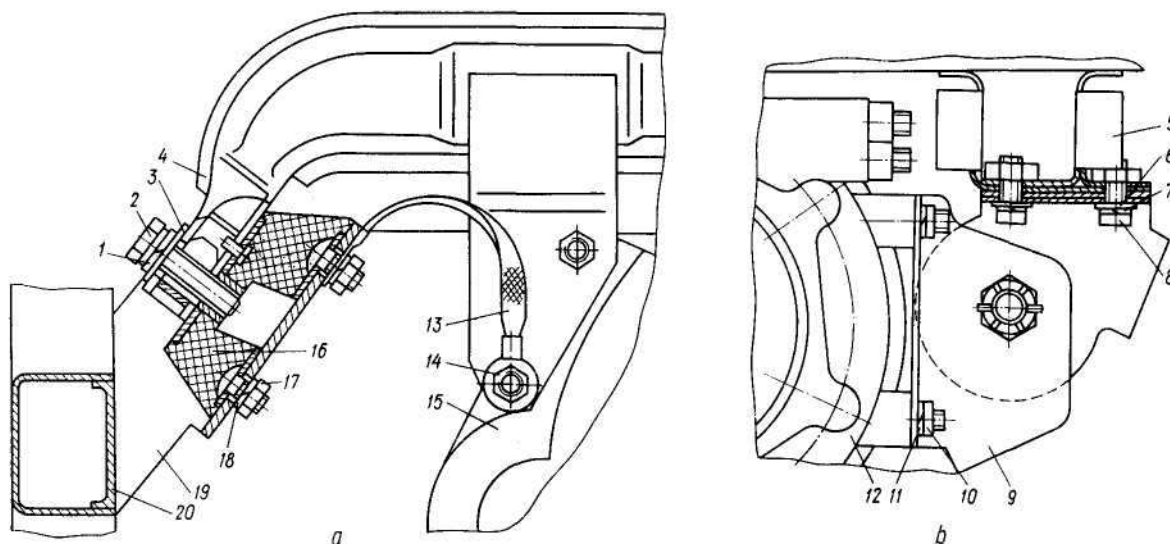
Крепление силового агрегата в сборе с приводным валом и редуктором заднего моста:
